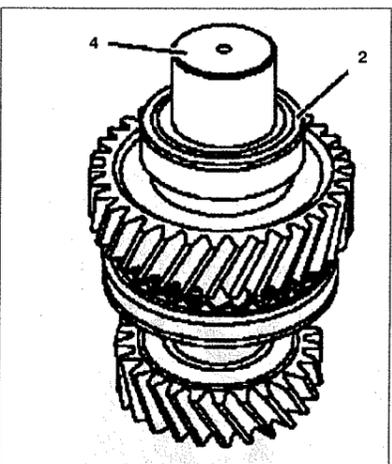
Установка роликового подшипника (автомобили с двигателями 611.980):
